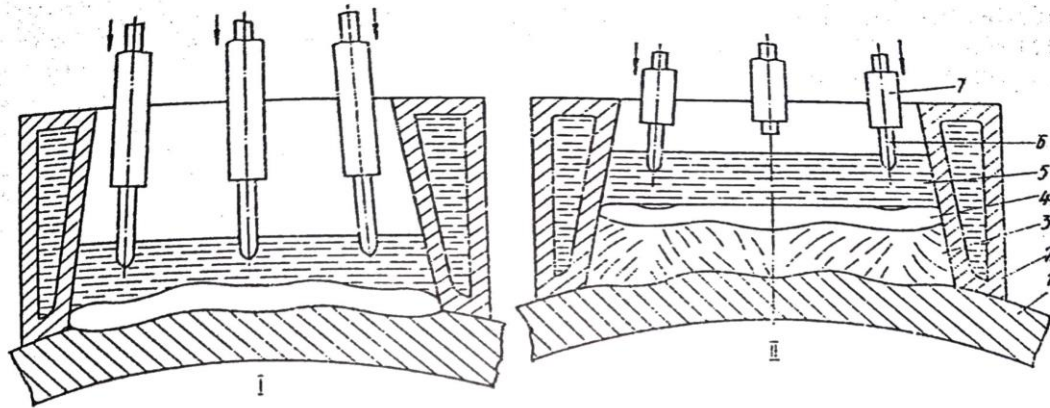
ЕШН припливів на поверхні тіл обертання: 1 – заготовка, що наплавляється; 2 – нерухомий водоохолоджуваний кристалізатор; 3 – наплавлений шар; 4 –металева ванна; 5 – шлакова ванна; 6 – електрод; 7 - мундштук
